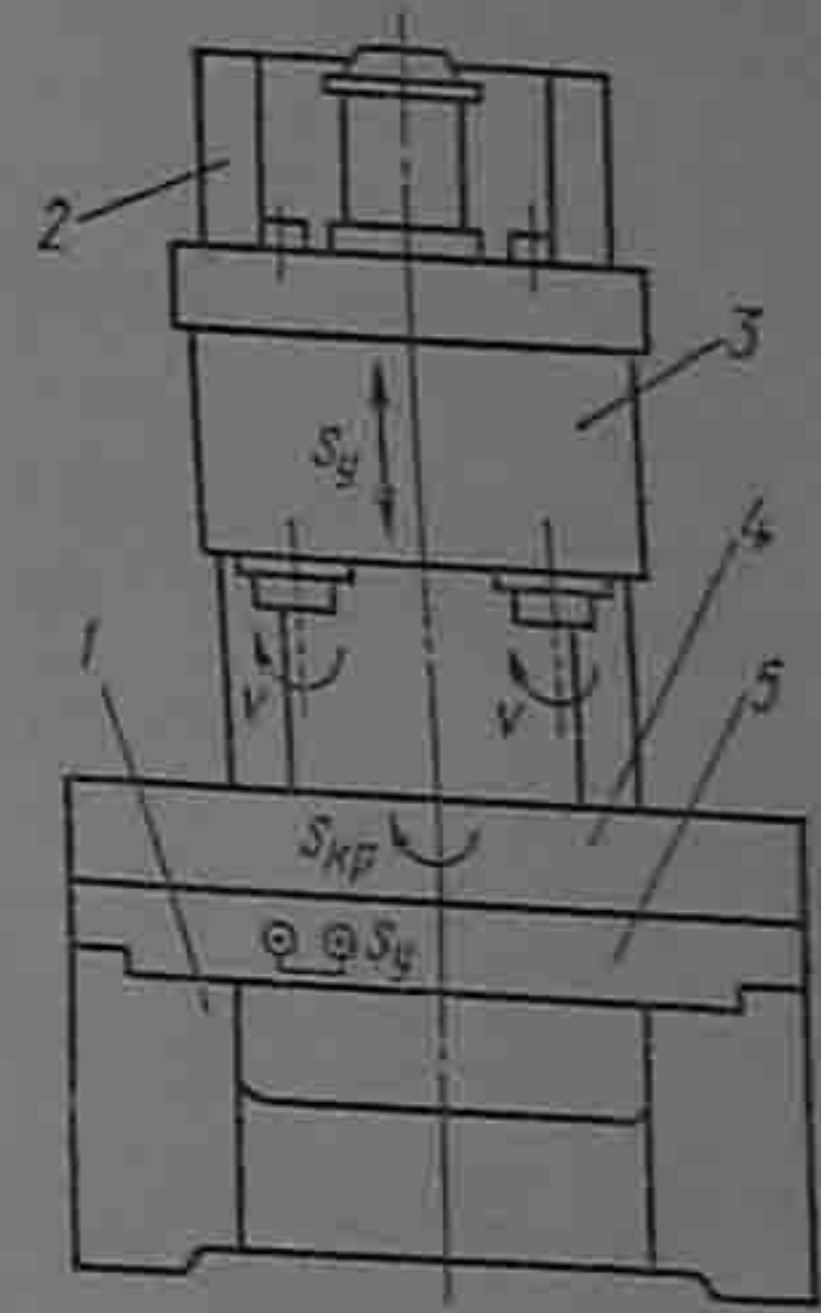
Общий вид двухшпиндельного карусельно-фрезерного станка
